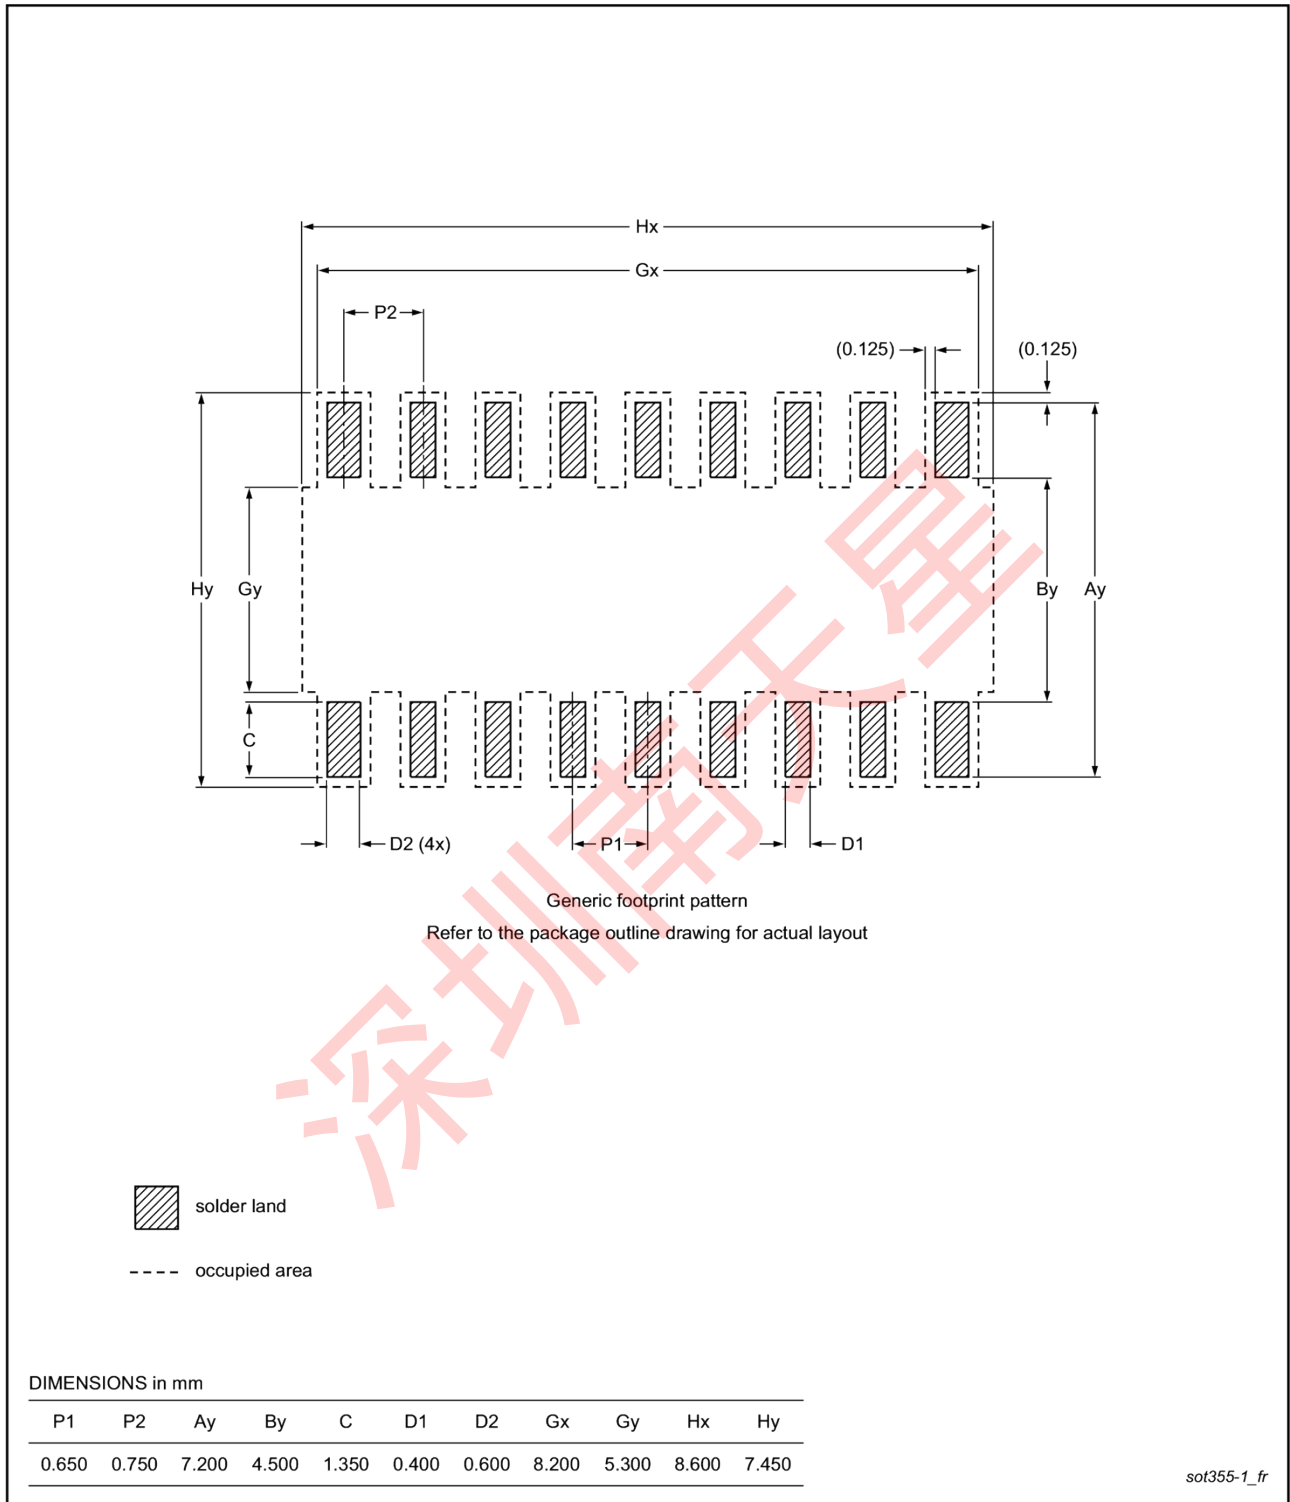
SOT355-1 (TSSOP24) 的 PCB 足迹; 回流焊接
